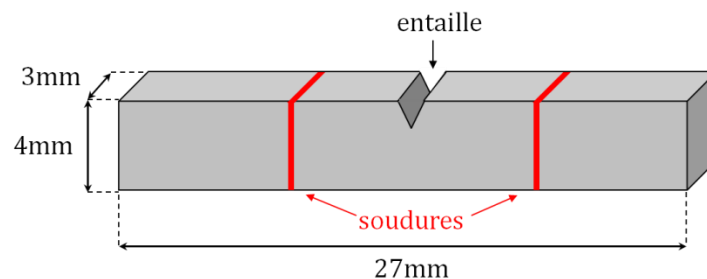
Schéma d'une éprouvette mini-Charpy reconstituée par soudage.
